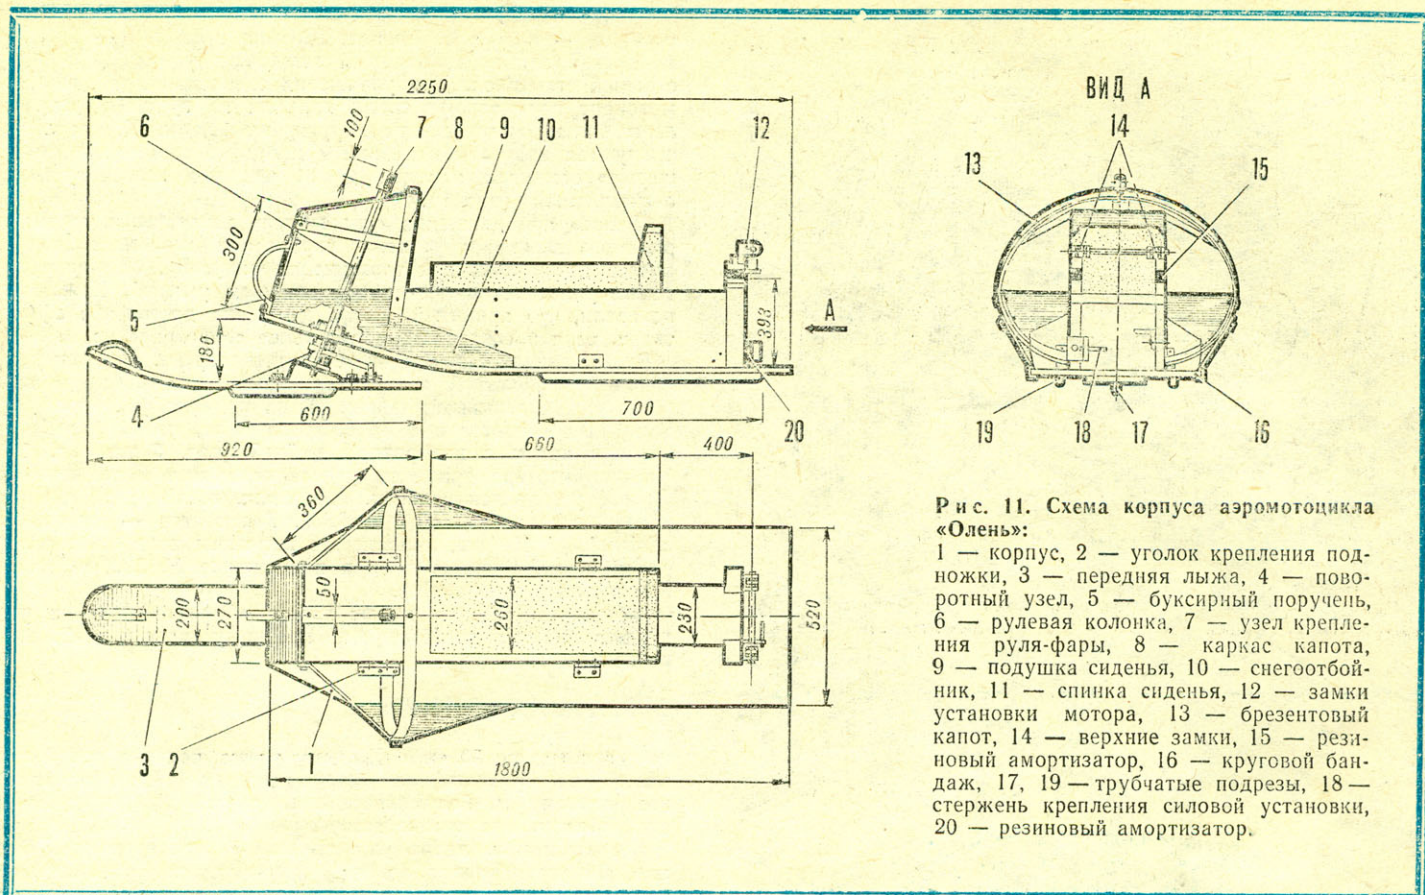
Схема корпуса аэромоторцикла «Олень»:
